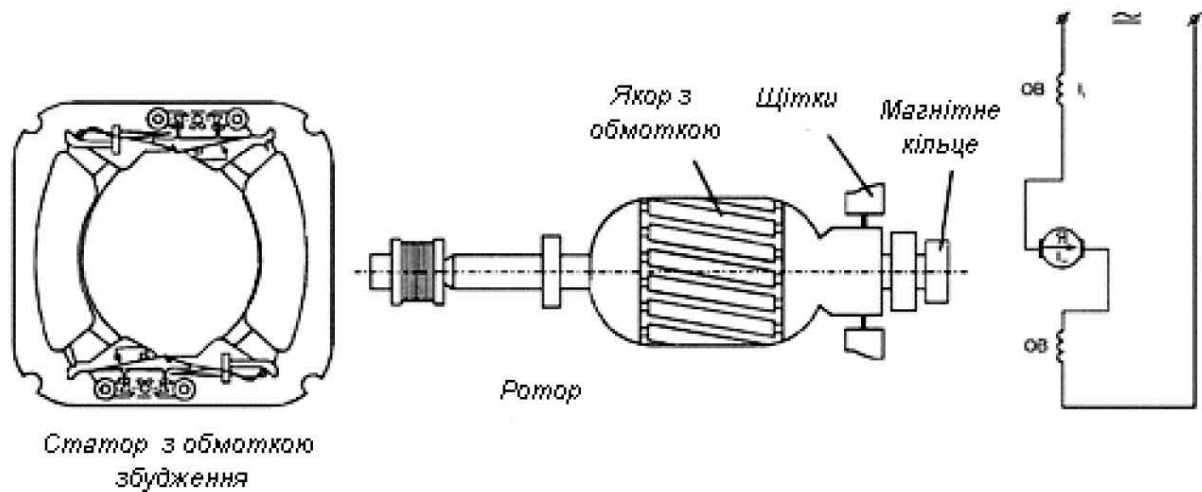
Побудова і принципова схема колекторного двигуна
